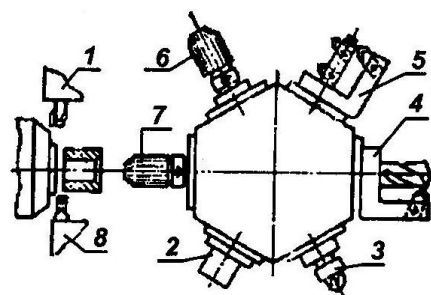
Схема налагодження токарно-револьверного верстата для виготовлення гладкої втулки
